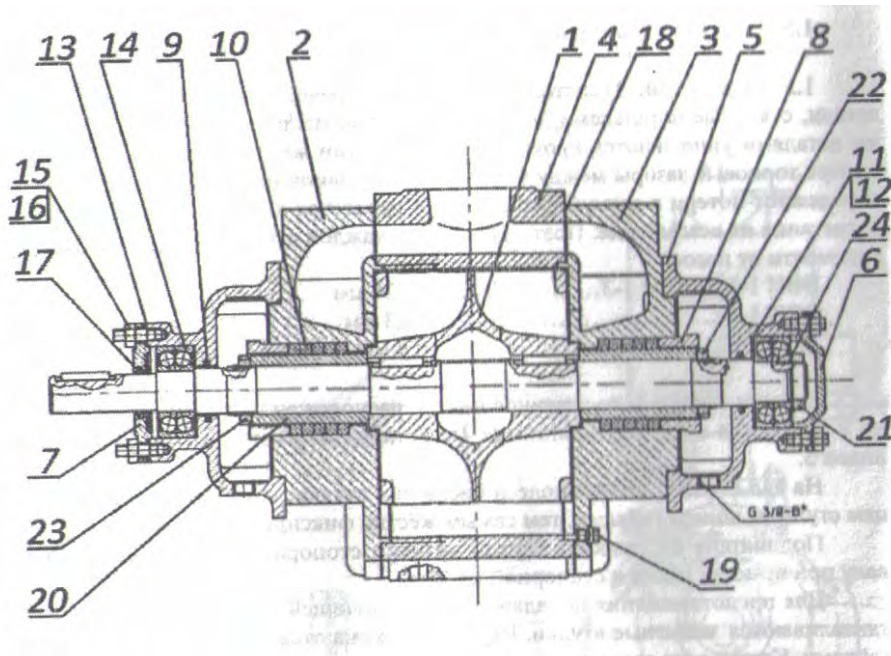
Общий вид водокольцевого вакуумного насоса: 1- ротор; 2 – лобовина левая; 3 – лобовина правая; 4 – корпус; 5 – корпус подшипника; 6 – крышка глухая; 7 – крышка открытая; 8 – букса сальника; 9, 17 – кольцо; 10 – сальниковая набивка; 11, 12 – кольцо дистанционное; 13, 18 – прокладка; 14 – подшипник; 15 – гайка; 16 – шпилька; 19 – пробка; 20 – втулка; 21, 22, 23 – гайка; 24 – шайба стопорная.
